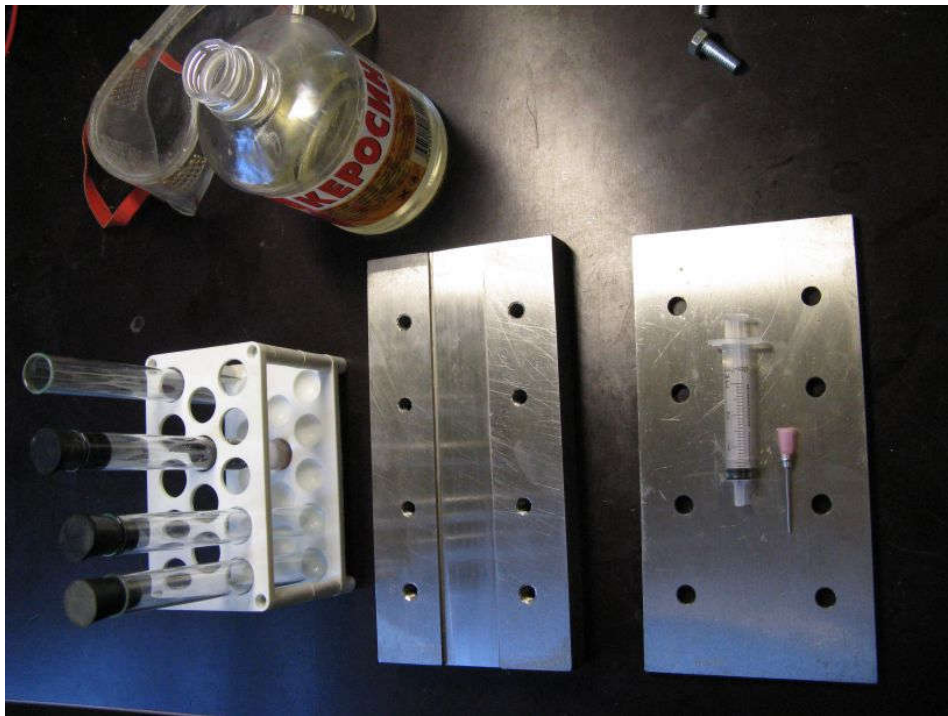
Инструментарий для изготовления литевых металлических макрочастиц: пресс для лития, полая игла для вырезания цилиндров, шприц для выдавливания полученных образцов из иглы, комплект пробирок.
